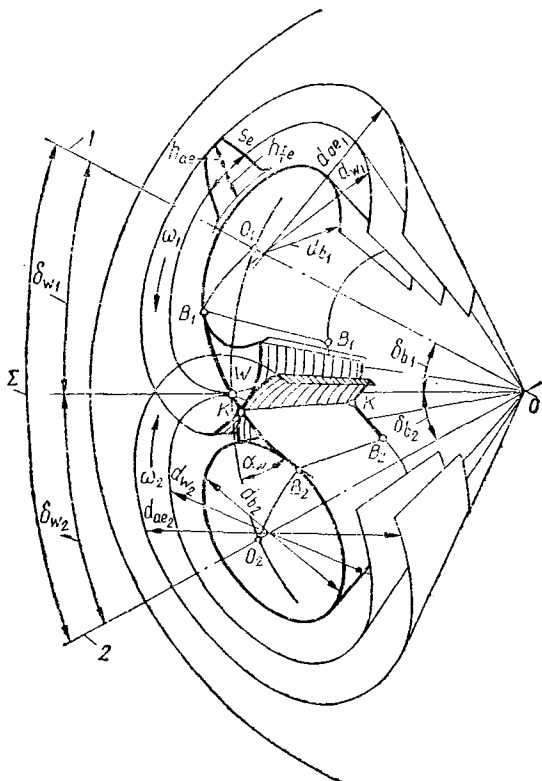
Основные параметры механизма с коническими зубчатыми колесами
